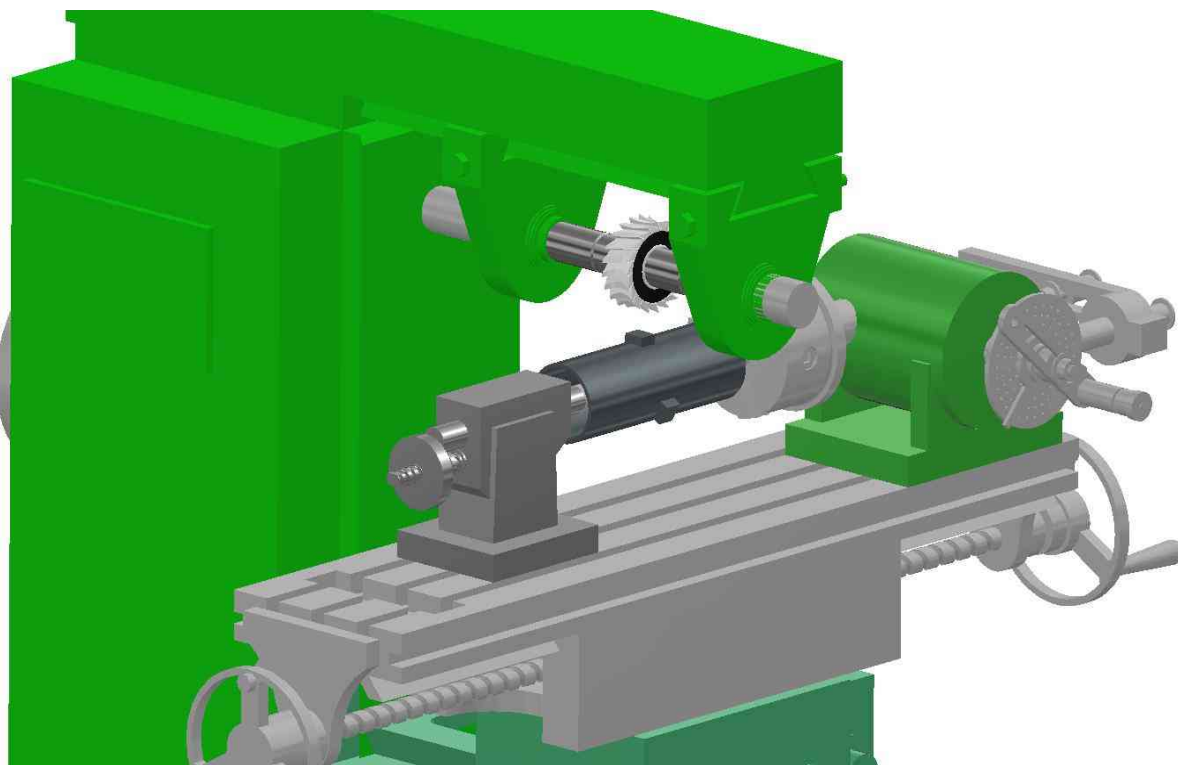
Фрезерування обічайки камери виробу РК-3 на консольно-фрезерному верстаті 6Р81
